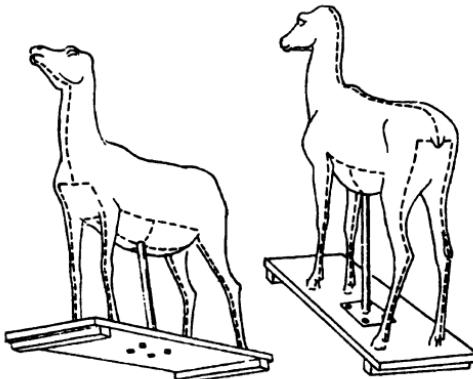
Фигура животного в глине с условными линиями для установки металлического бортика при формовке.
